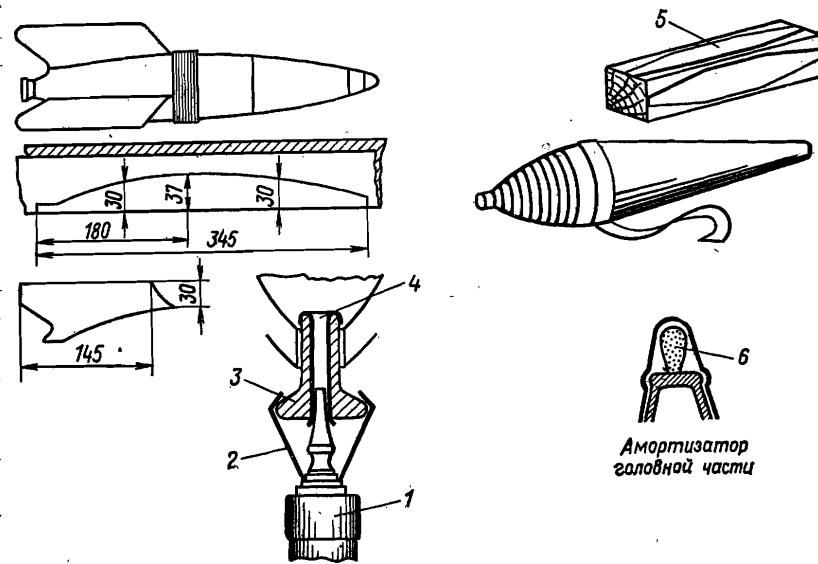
Изготовление воздушно-гидравлической модели ракеты.
